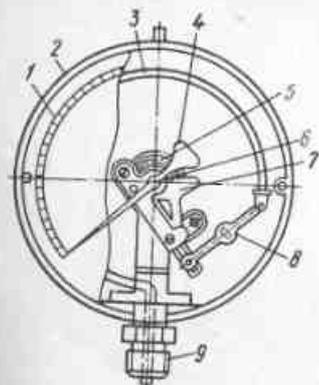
Устройство показывающего манометра с одновитковой пружиной
